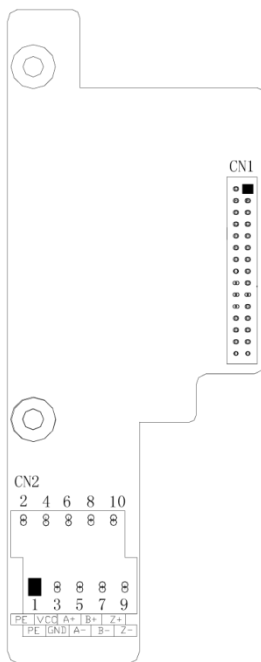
Чертеж по габаритным размерам В-PG01, В-PG02
